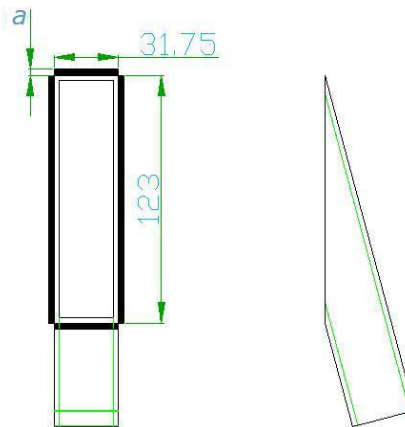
Geometría del cordón de soldadura del soporte del ventilador
